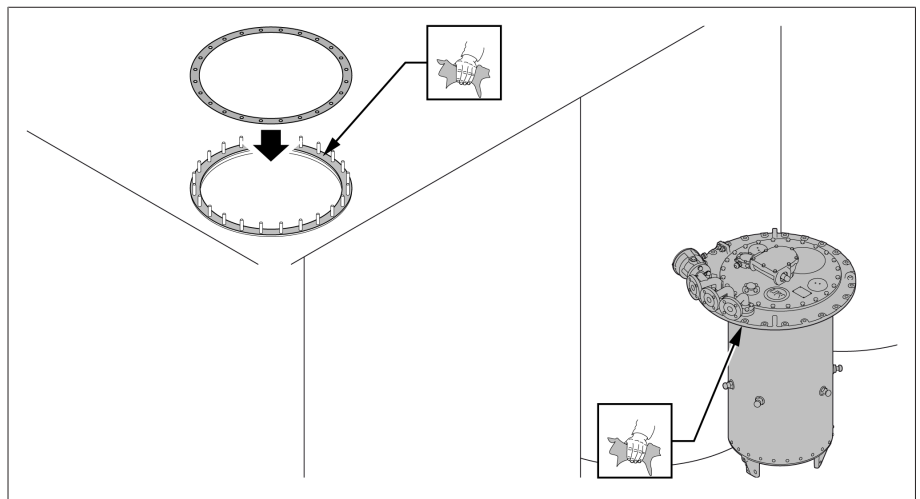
Surfaces d'étanchéité, joint d'étanchéité
